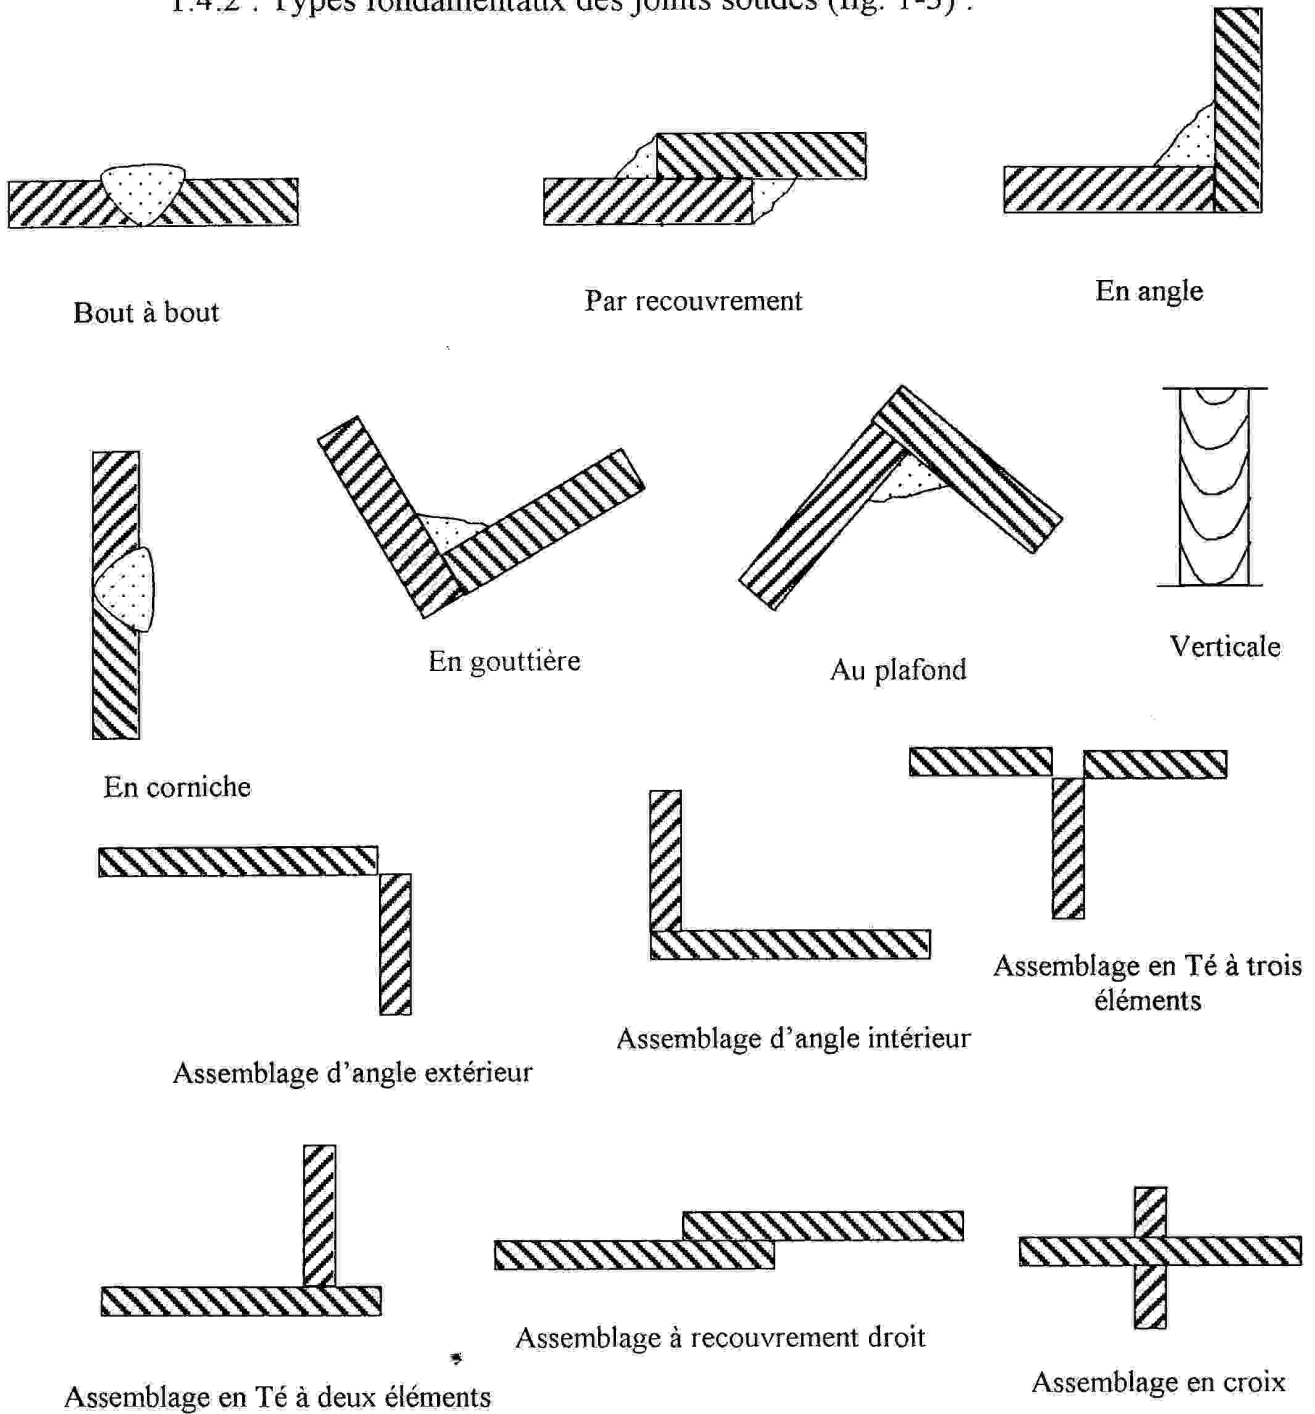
types fondamentaux des joints soudés [3]
